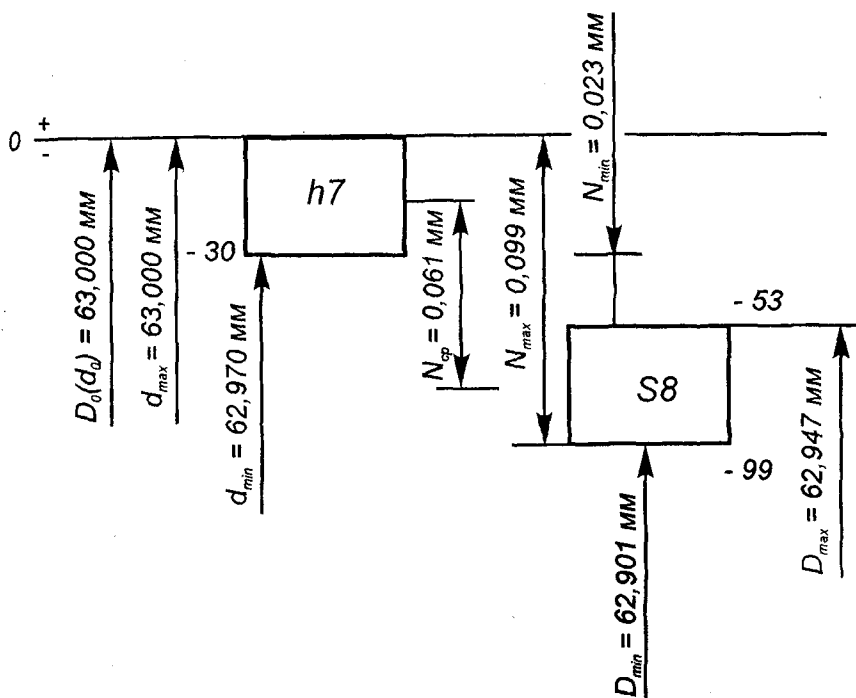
Схема расположения полей допусков сопрягаемых деталей
